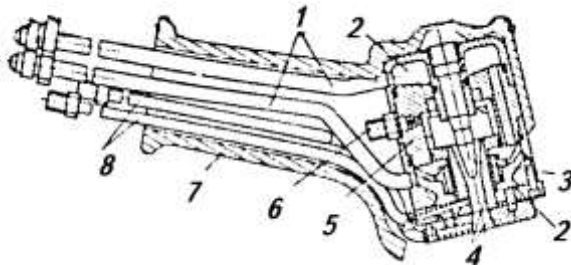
Схема конструкции электродугового плазмотрона: 1 – подвод постоянного тока и охлаждающей воды; 2 – вода; 3 – катод; 4 – анод; 5 – изолятор; 6 – рабочий газ; 7 – рукоятка; 8 – порошок
